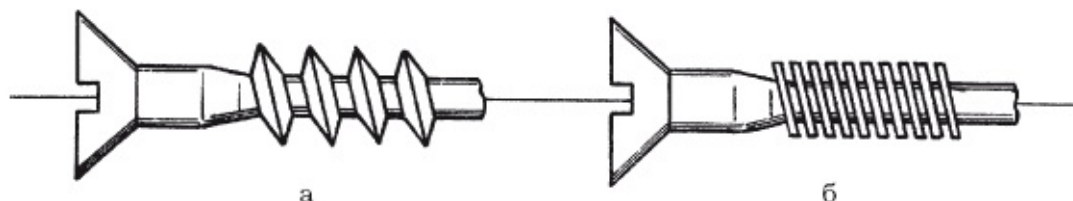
Шурупы различных видов: а – с острой резьбой; б – с тупой резьбой
